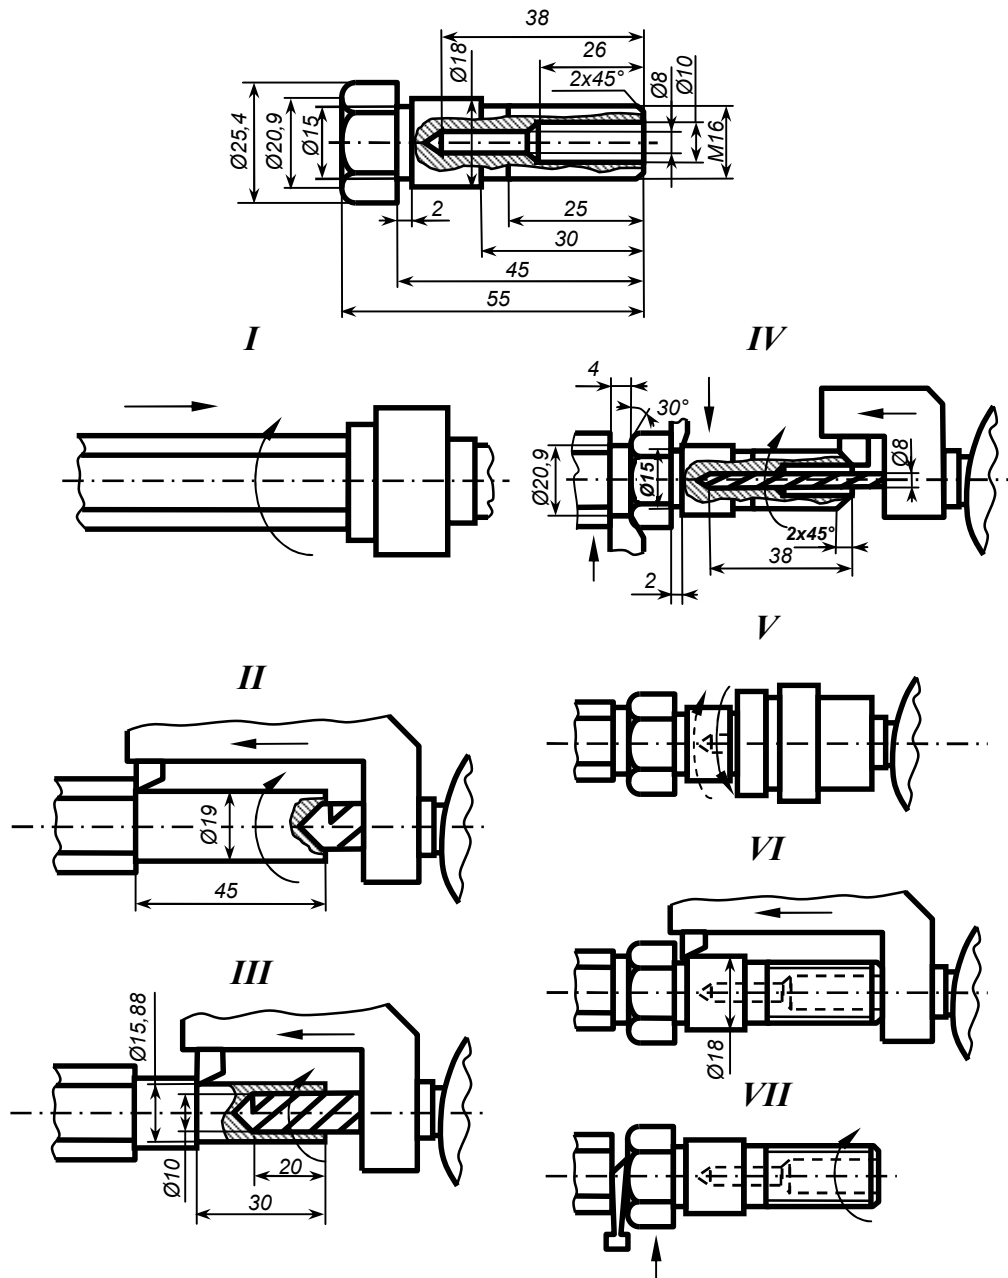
Схема наладки для обробки пробки на токарно-револьверному автоматі:
